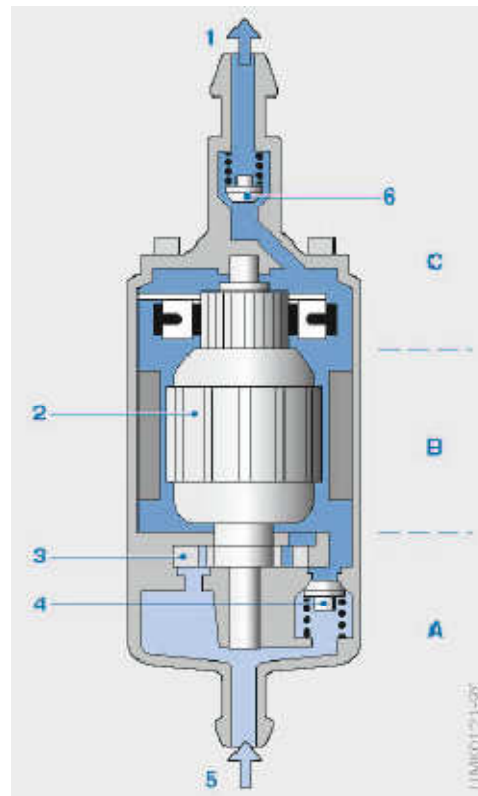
Proudění paliva v zubovém čerpadle [3]
